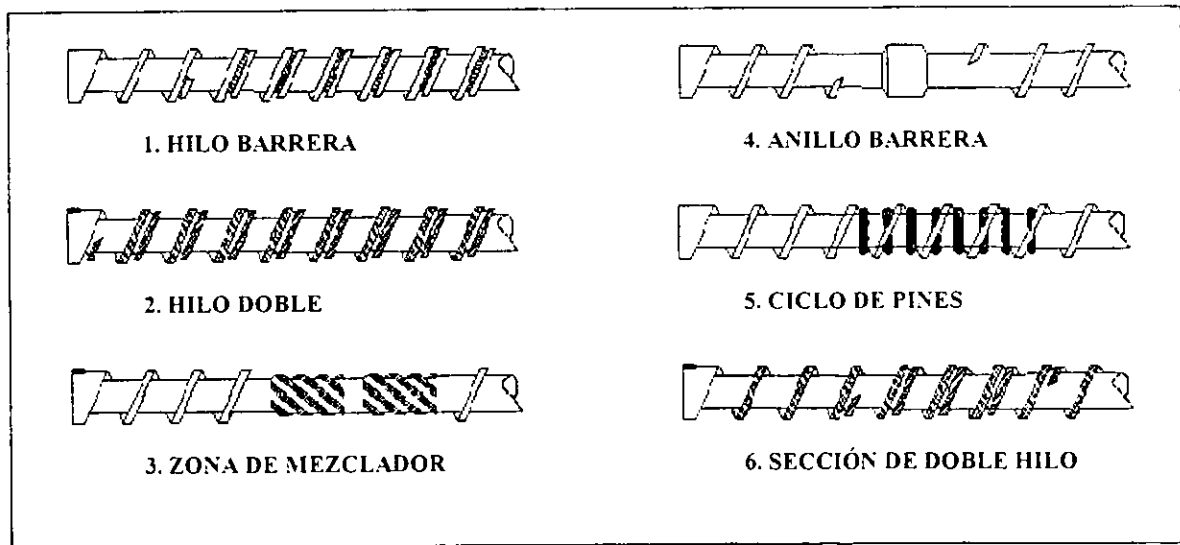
Diferentes diseños de zonas de Compresión.
